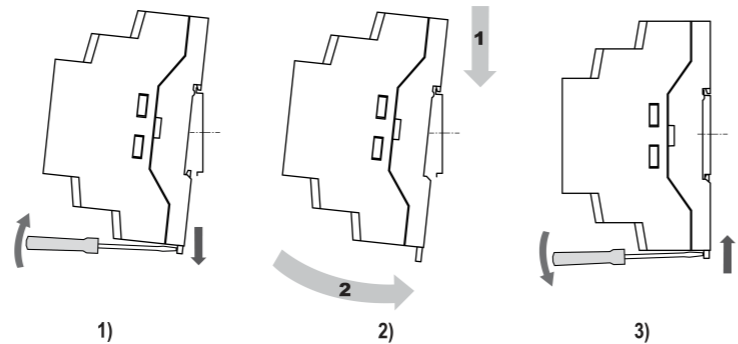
Монтаж прибора с креплением на DIN-рейку
